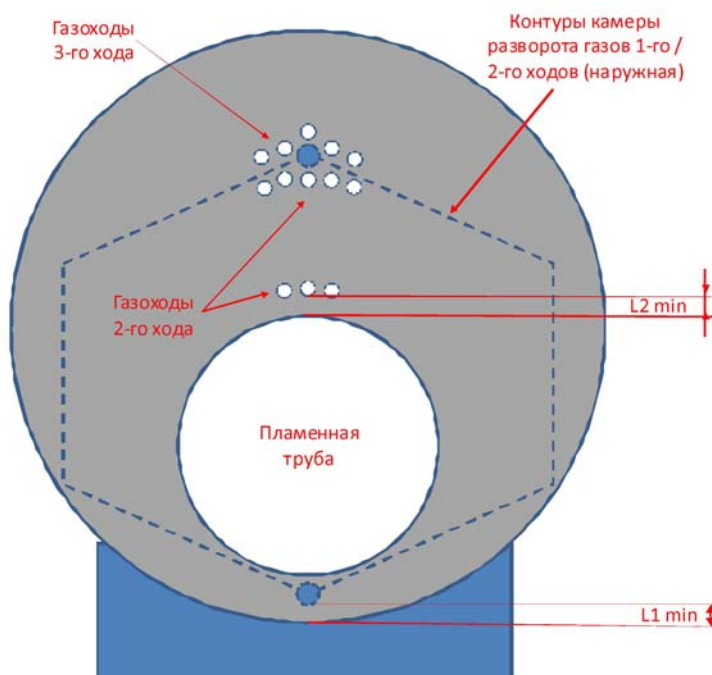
Котёл с наружной камерой разворота газов (вид спереди)
